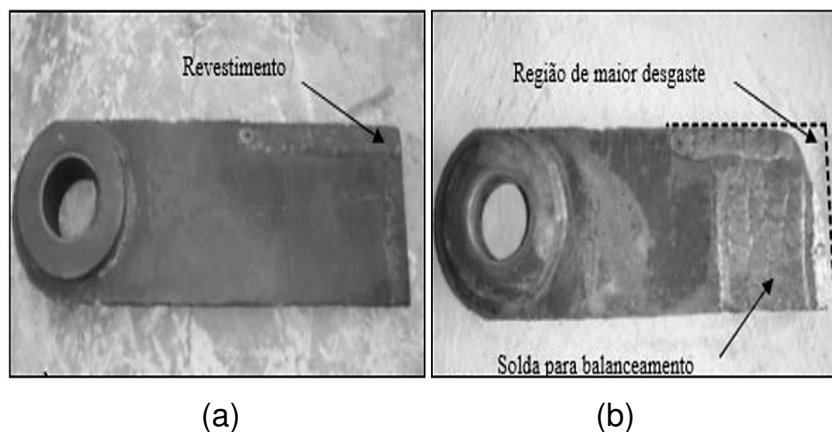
Imagem do martelo oscilante (a) desgastado e (b) recuperado por soldagem de revestimento duro.
